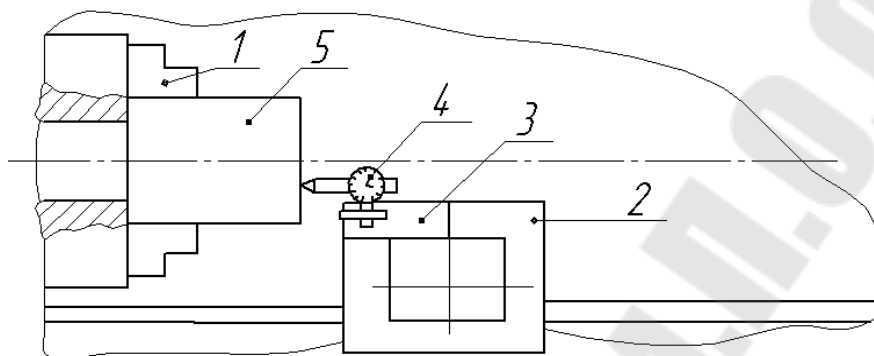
Схема измерения погрешности закрепления заготовки:
